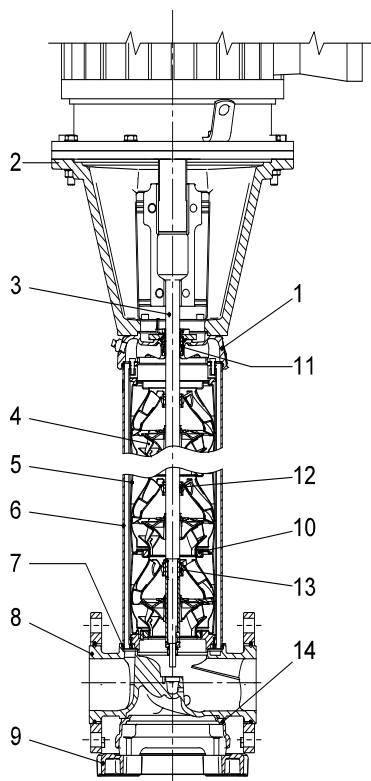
Schnittzeichnung einer CR(N)-Pumpe
